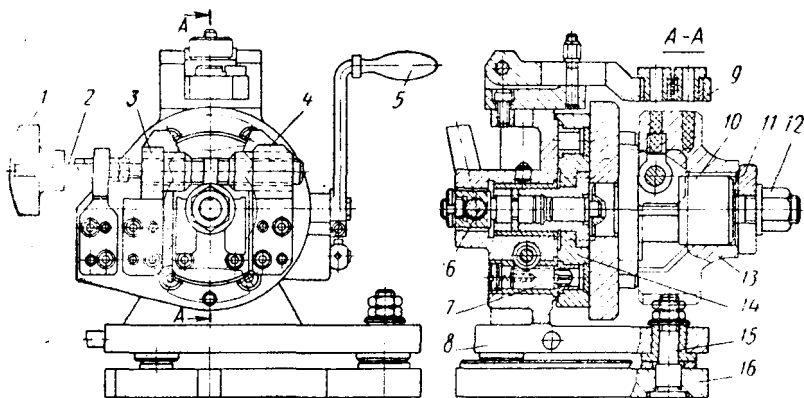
Поворотное и передвижное приспособление для крепления вилок при обработке на вертикально-сверлильном станке
